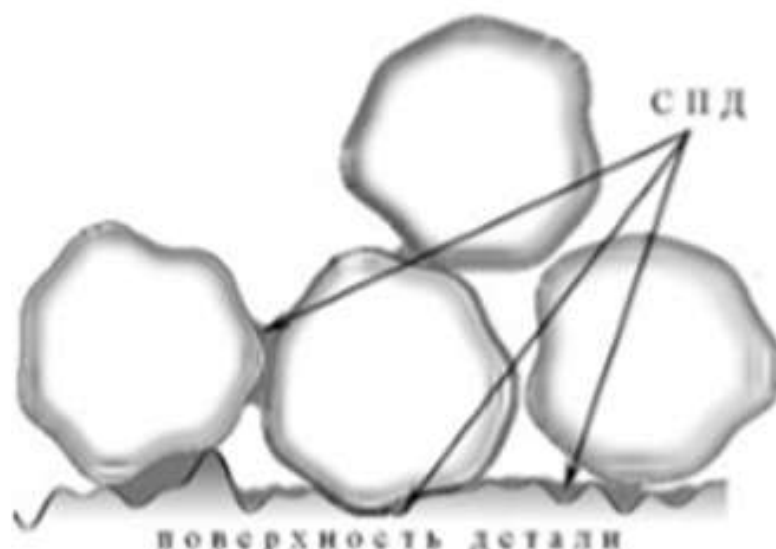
Схема воздействия гранул свободного абразива на поверхность детали
